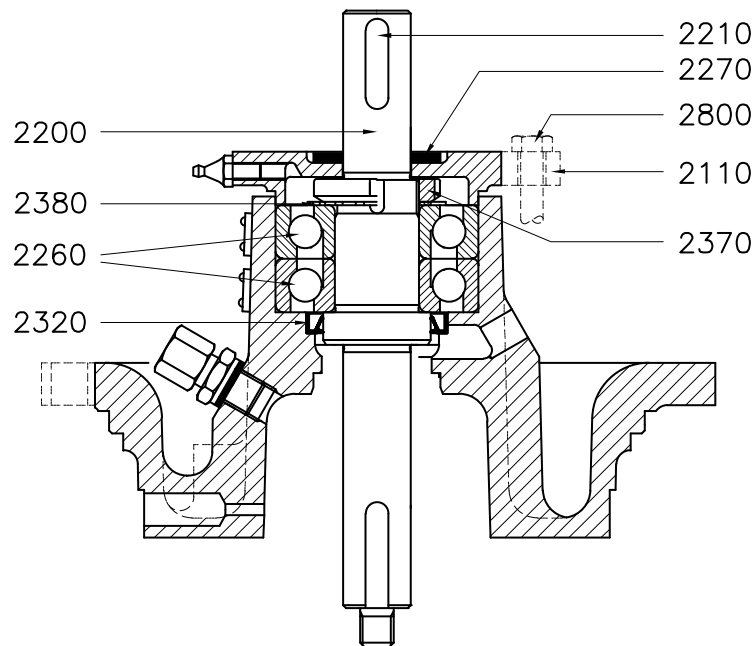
Разборка подшипников, консольных опор для подшипника 1, 2 и 3.
